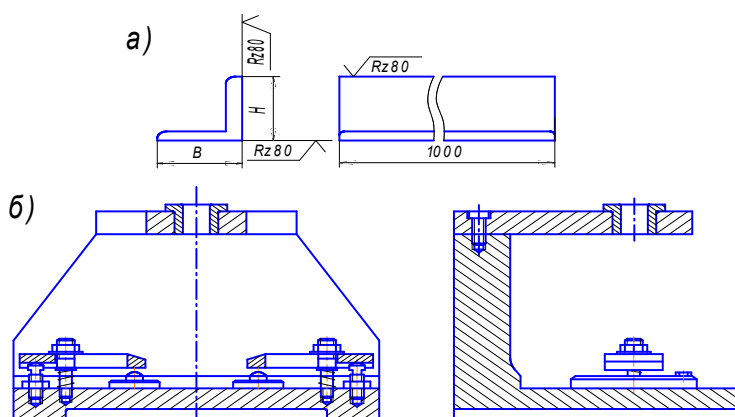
Заготовка корпуса приспособления из угольника (а) и применение его в приспособлении (б)
